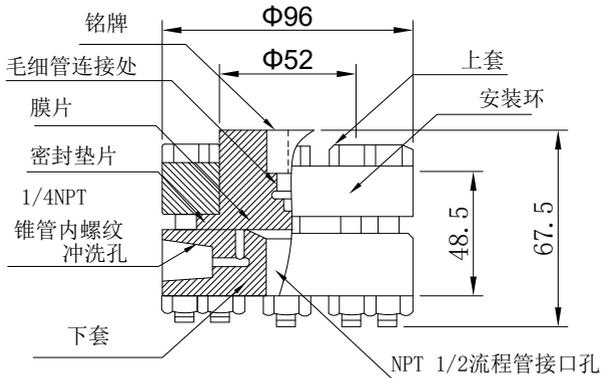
RTW 型螺纹安装式远传装置外形尺寸图
